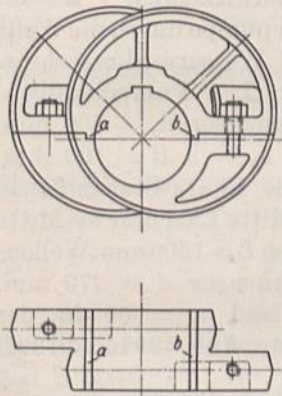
Doppel-exzenter mit kegeligen Laufflächen.
